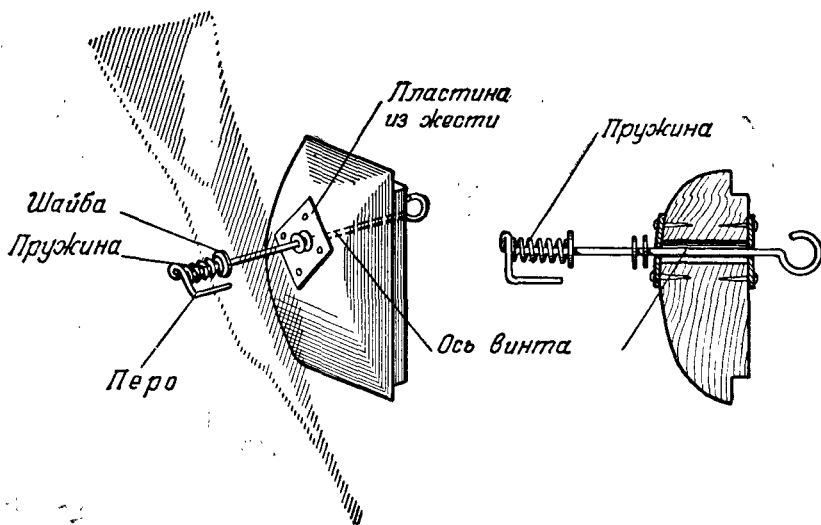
Бобышка и подшипник винта. Справа — разрез бобышки
